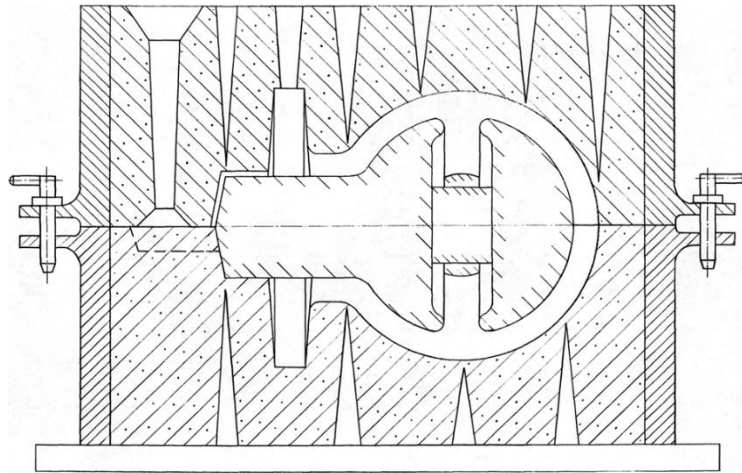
Разрез опочной формы для отливки корпуса вентиля
